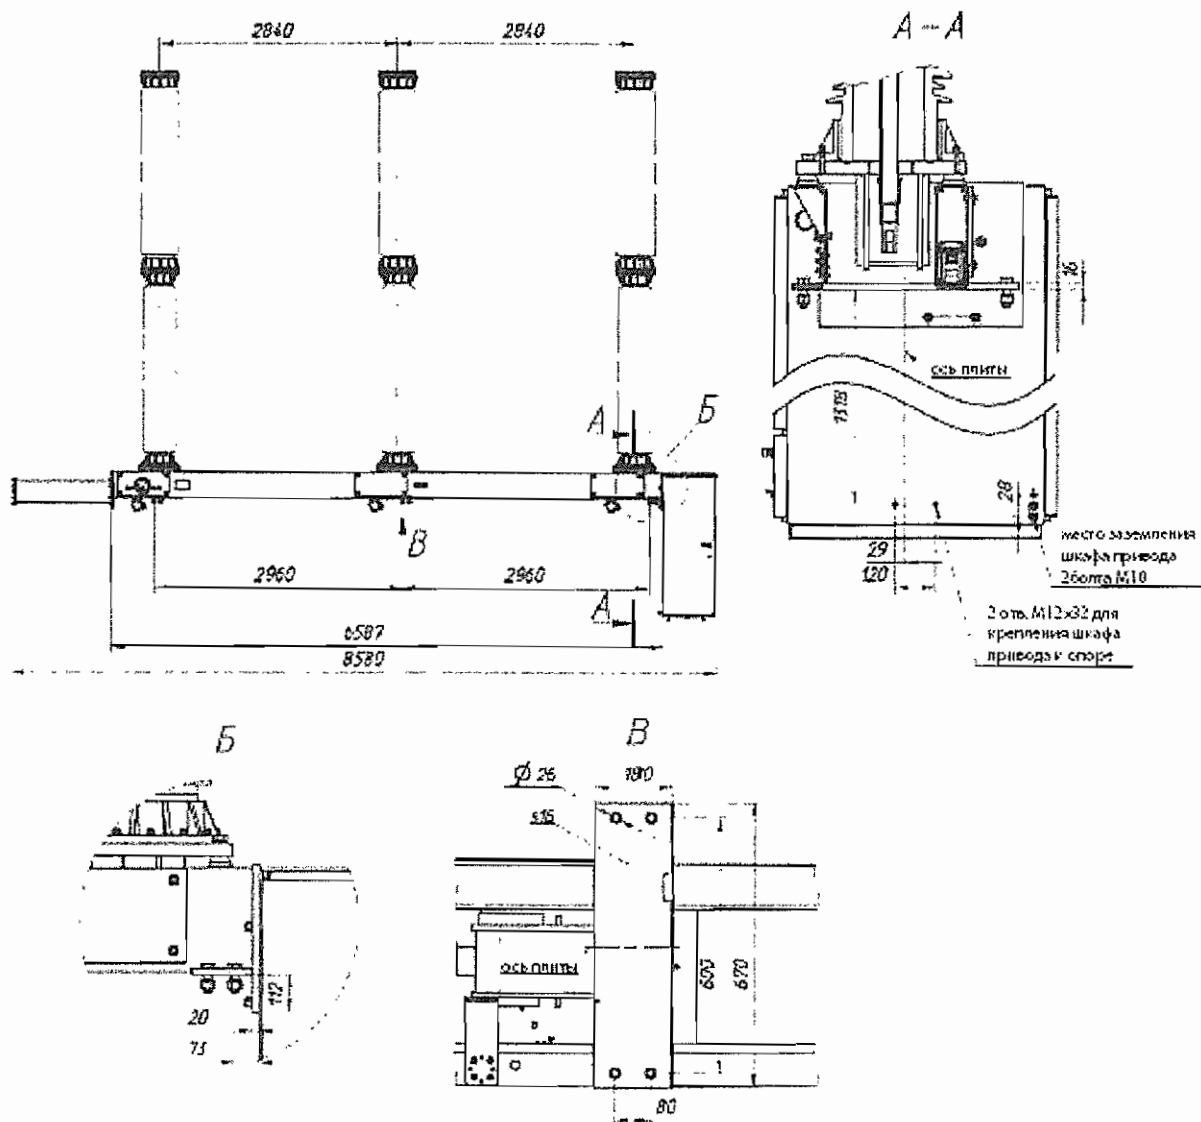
Габаритные и установочные размеры выключателя ВГТ-1А1-220* в исполнении без опорных металлоконструкций.
